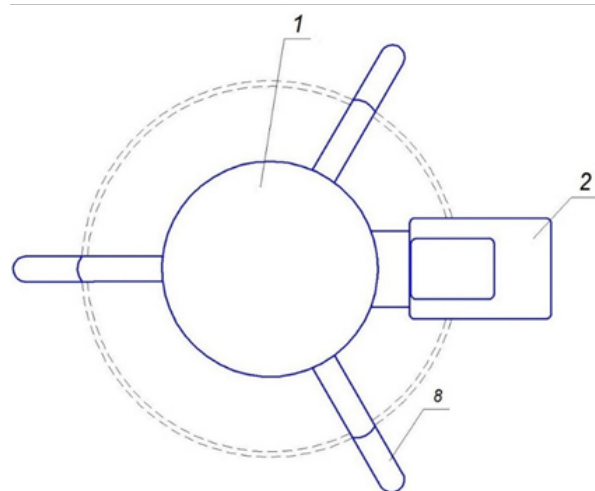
Мясорубка с вертикальным расположением шнека (вид сверху)
